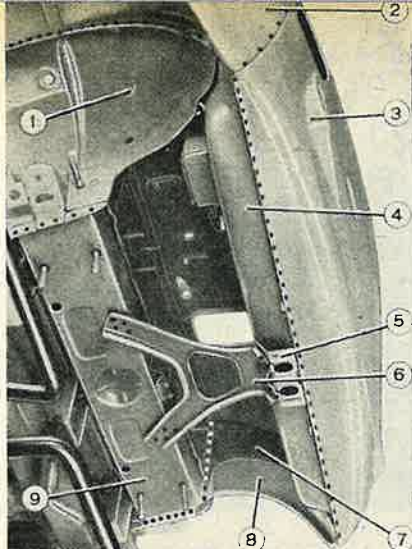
Liaisons par points de soudure de la partie avant du plancher.
